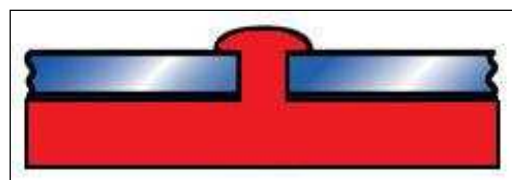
INTEGRACIÓN POR COMPRESIÓN: UNIÓN POR MOLDEO POR INYECCIÓN
